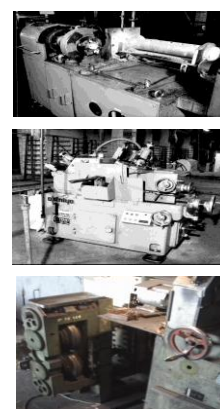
Складові технологічного обладнання виготовлення стрічок із тугоплавких металів
